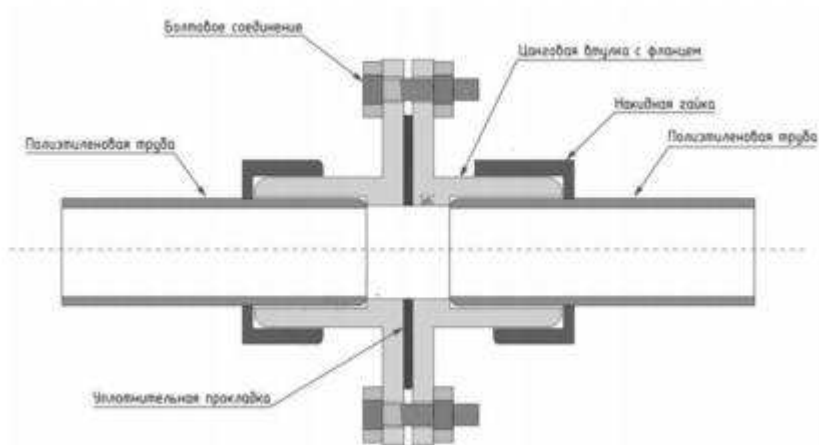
Схема фланцевого соединения пластиковых труб
